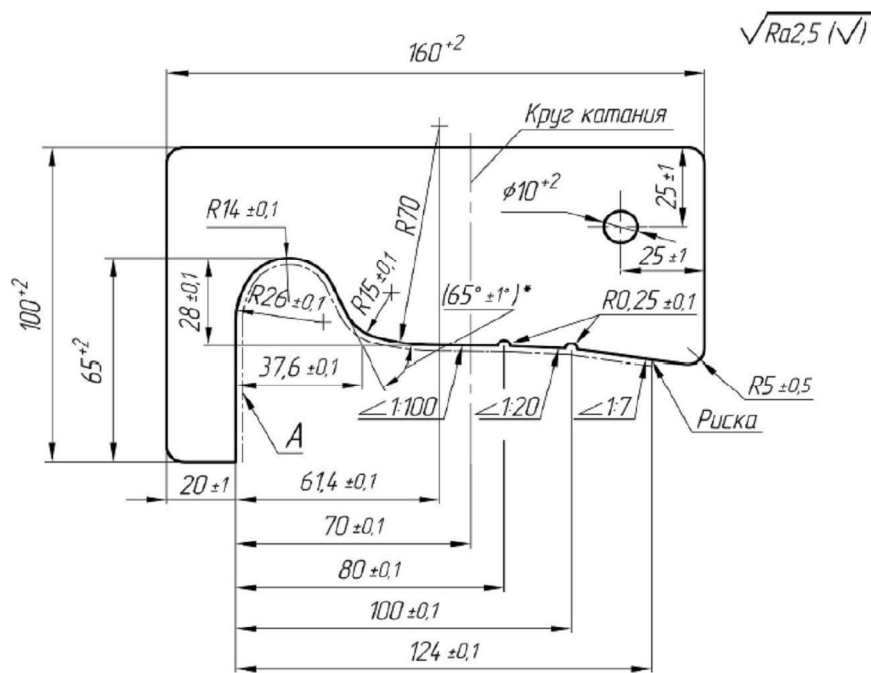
Профиль обода колеса и максимальный шаблон для его проверки
